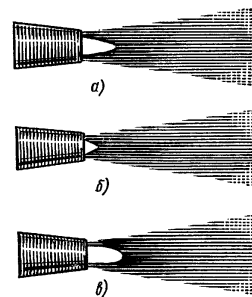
Схема строения сварочного газокислородного пламени:
